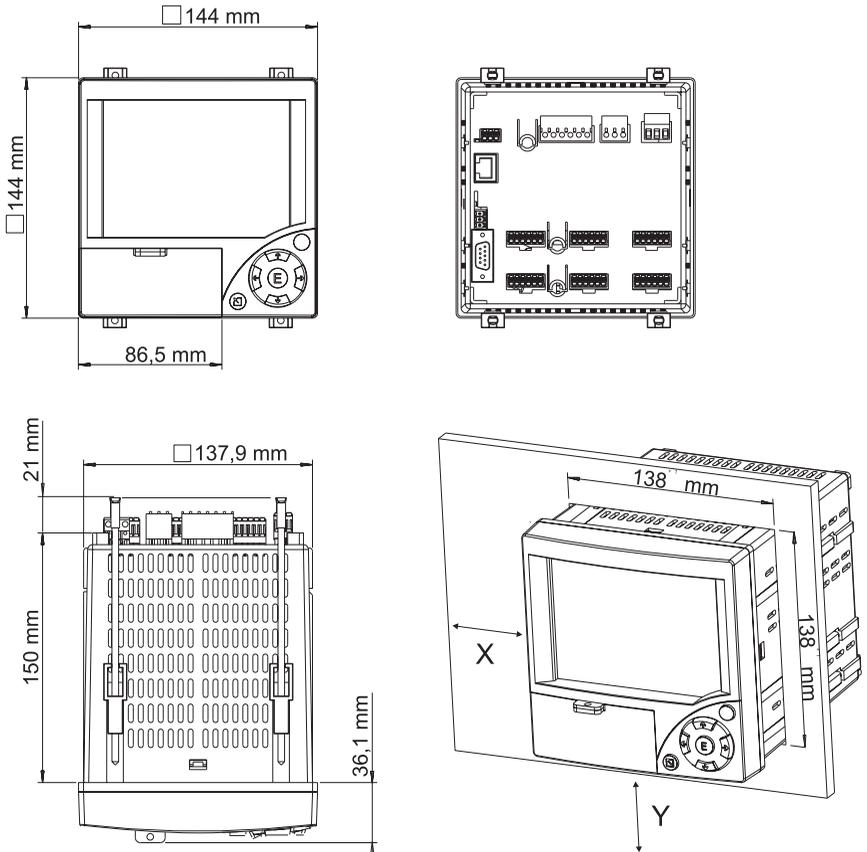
Installazione a fronte quadro e dimensioni di montaggio
